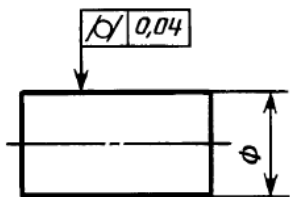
Допуск цилиндричности вала – - 0,04 мм
